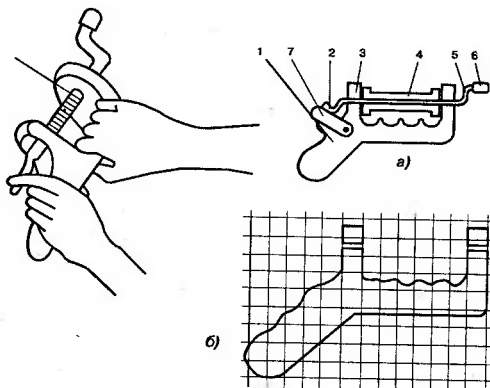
Устройство моталки (а) и чертеж ручки моталки (б):
